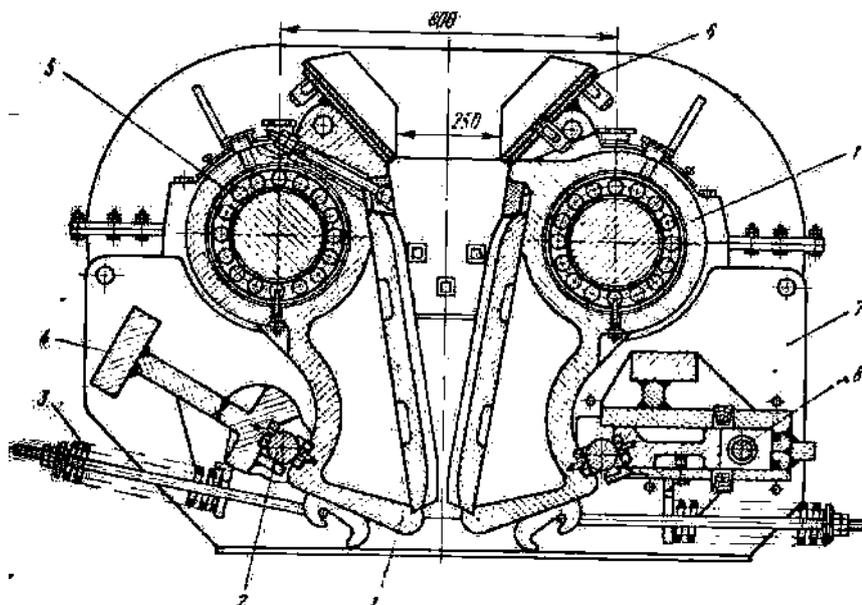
Щековая дробилка с двумя подвижными щеками;
